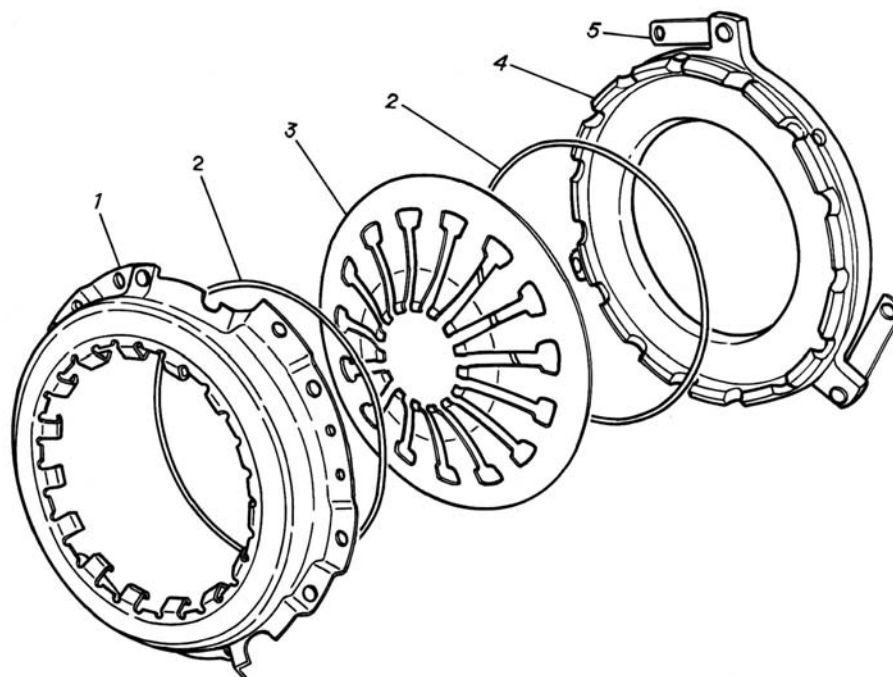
Детали ведущего диска: 1 - кожух; 2 - опорные кольца; 3 - нажимная диафрагменная пружина; 4 - нажимной диск; 5 - соединительная пластина
